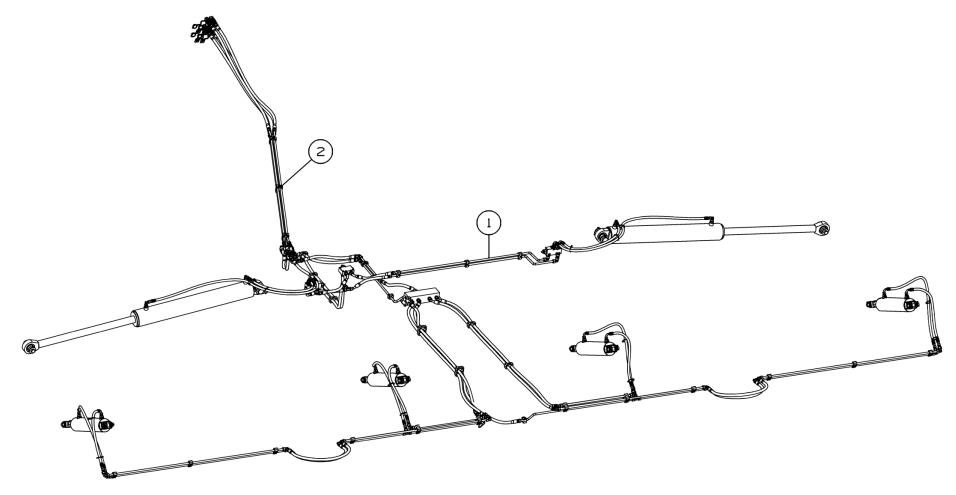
Установка гидрооборудования К-102.12.000Б
